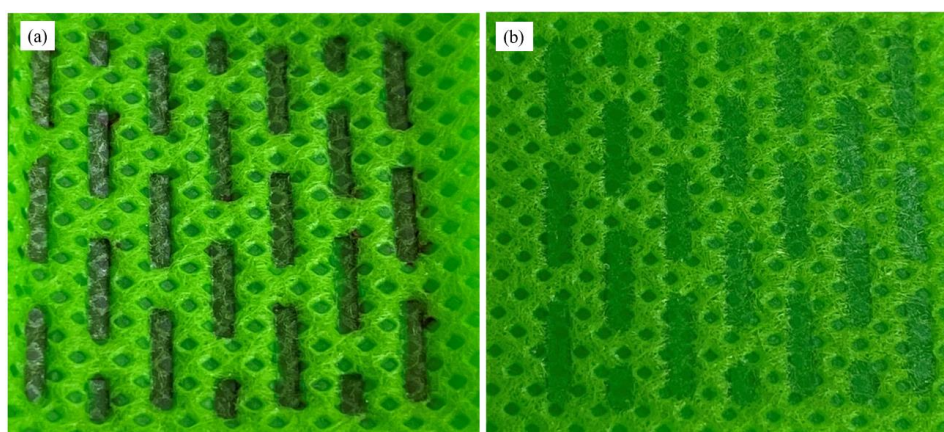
Tecido após realização de soldadura; (a) vista frontal, (b) vista de trás
